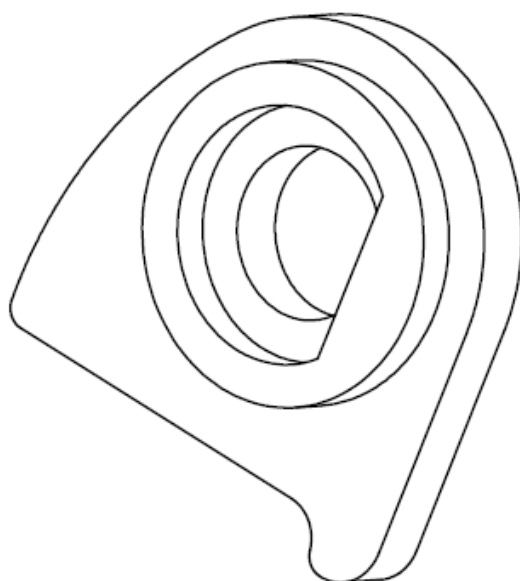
insieme presaldato della staffa destra per l'ancoraggio del cesto
